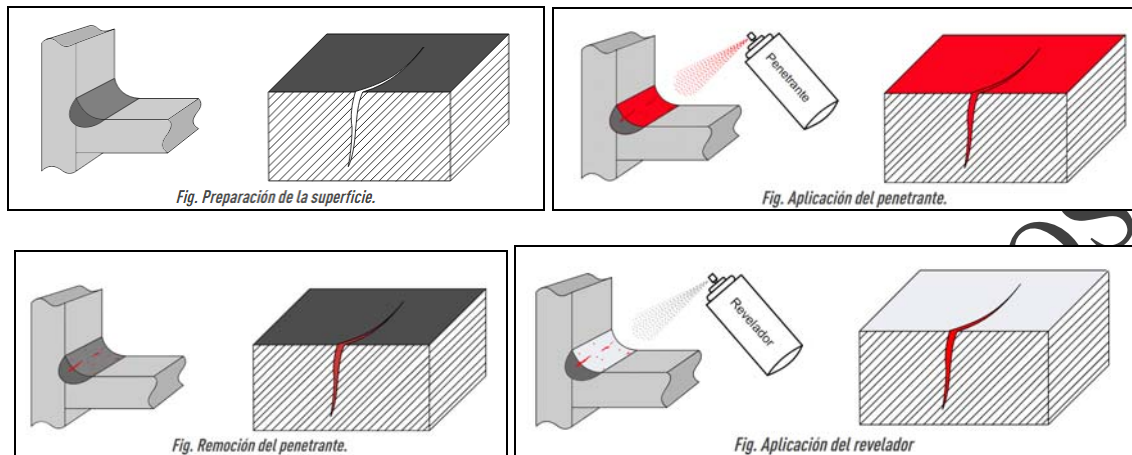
Aplicación de líquidos penetrantes a la soldadura
